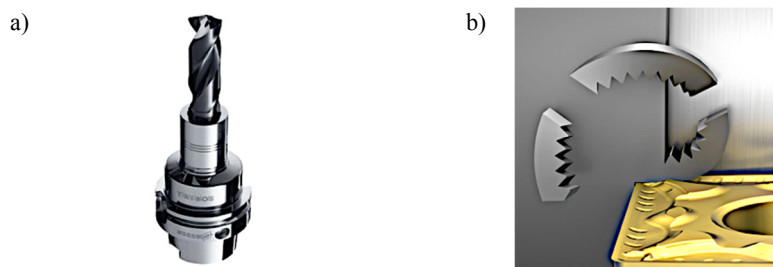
a) Ferramenta de corte de suporte integrado; b) Ferramenta de corte com quebra-apara [4].
